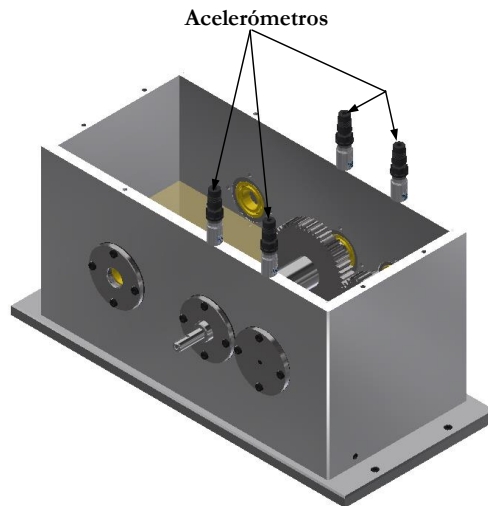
Ubicación de los acelerómetros en la caja de engranajes [Fuente: Autor].
